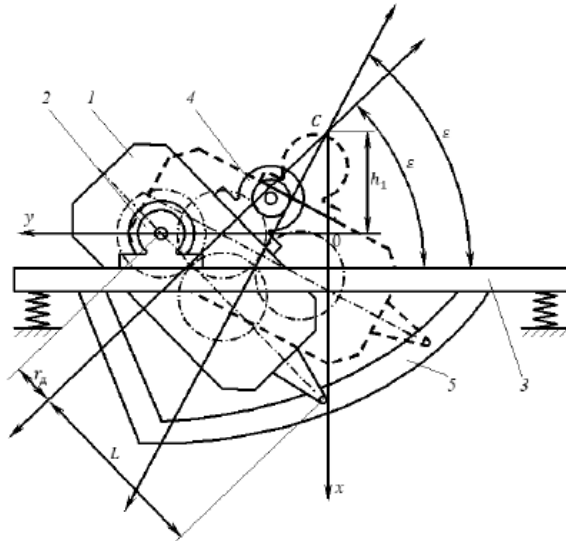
Схема компоновки привода при розбіжності ведучого валу вібробудувача з центром тяжіння частини що коливається:
